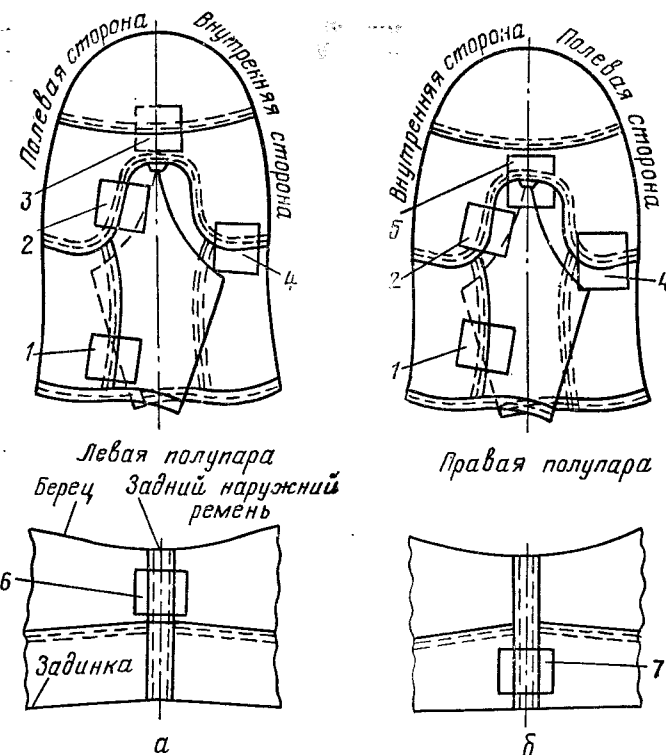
Расположение на заготовках верха полусапог, ботинок, полуботинок и туфель образцов для определения прочности швов левой (а) и правой (б) полупар:
